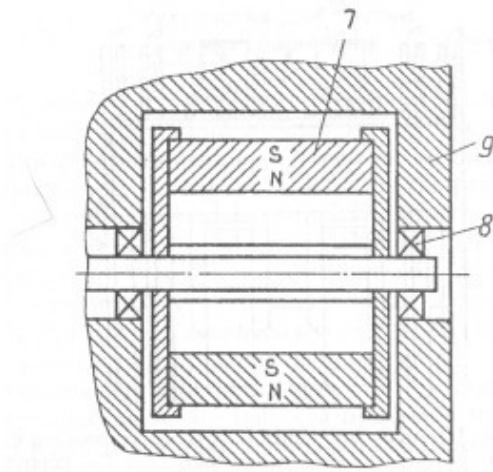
Поперечный разрез генератора переменного магнитного поля, см. Рис. 32, где 7 – магнитный ротор; 8 – подшипники; 9 – корпус (А-А повернуто).
